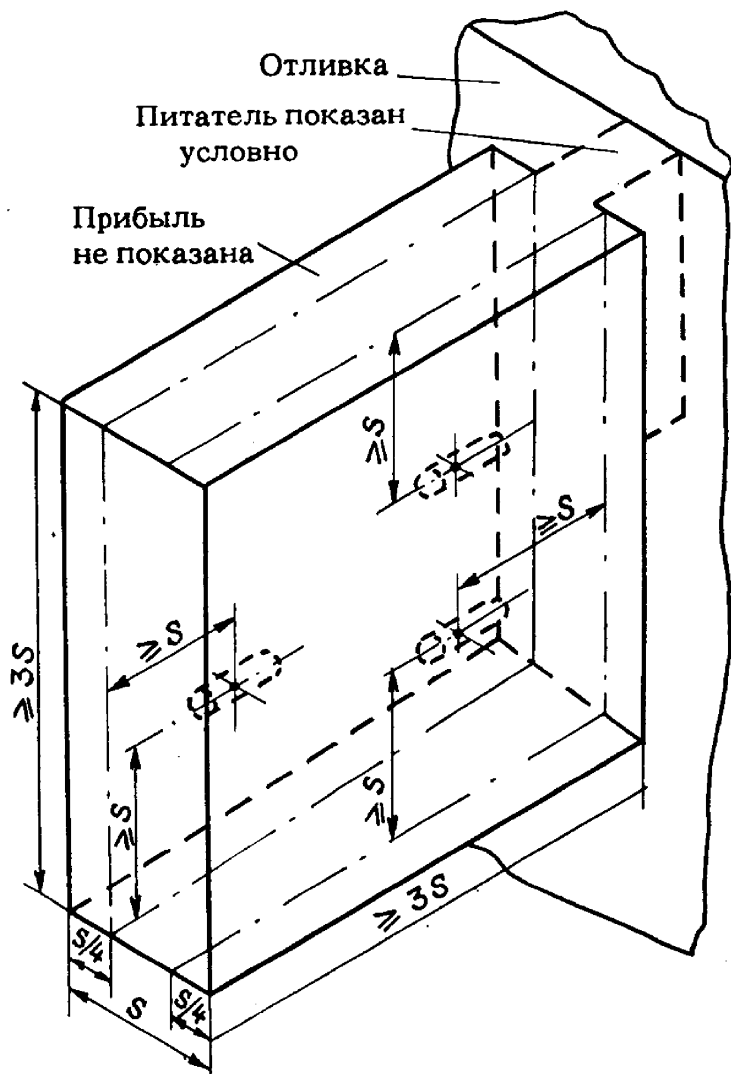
Схема отбора образцов для испытаний механических свойств из прилитой пробы
